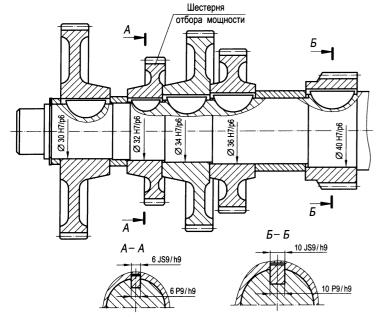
Соединение зубчатых колес с валом коробки передач сегментными шпонками
